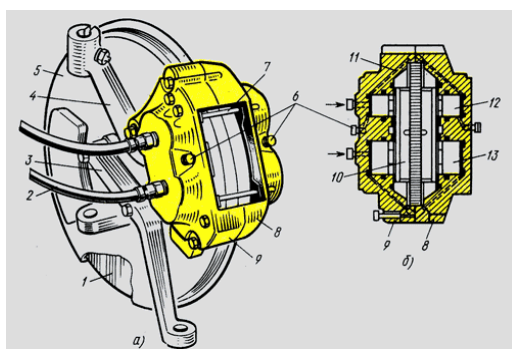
Колесный дисковый тормозной механизм с гидроприводом: а – в сборе, б - разрез по оси колесных тормозных цилиндров
